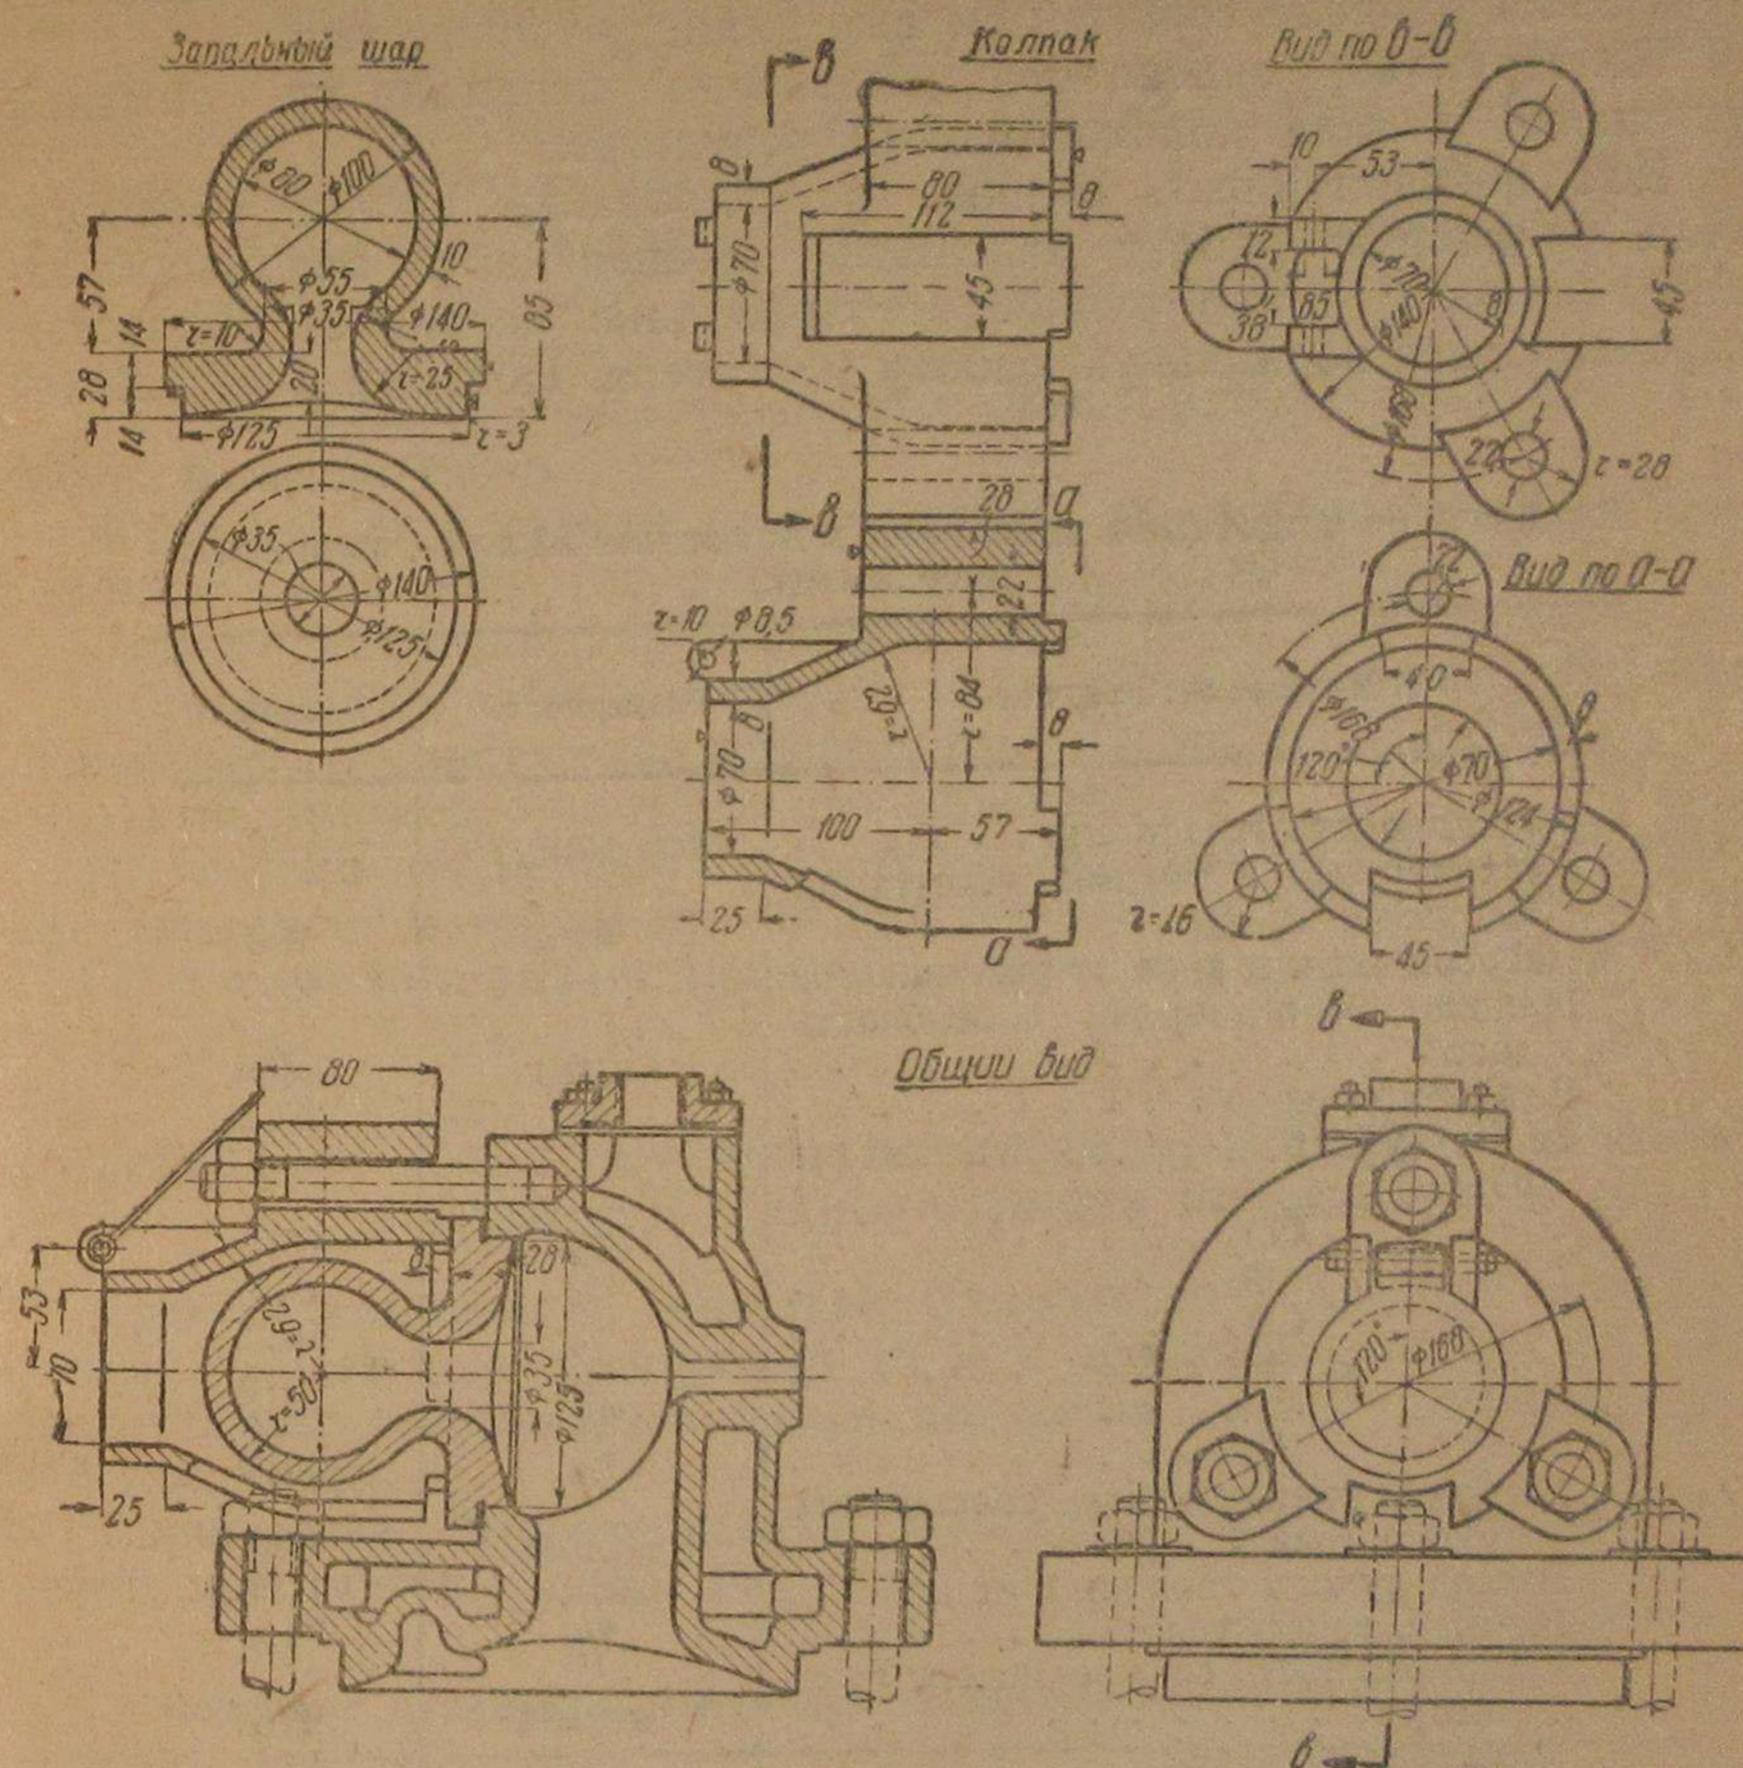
Общий вид и детали головки двигателя мощностью 22 л. с. завода имени Кирова (переведённого на газ)
